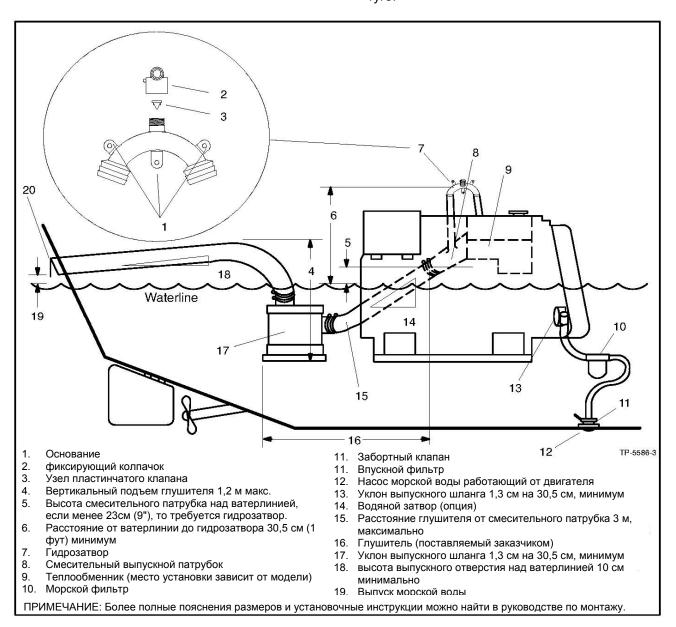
Гидравлический затвор (пластиковый типа U)
